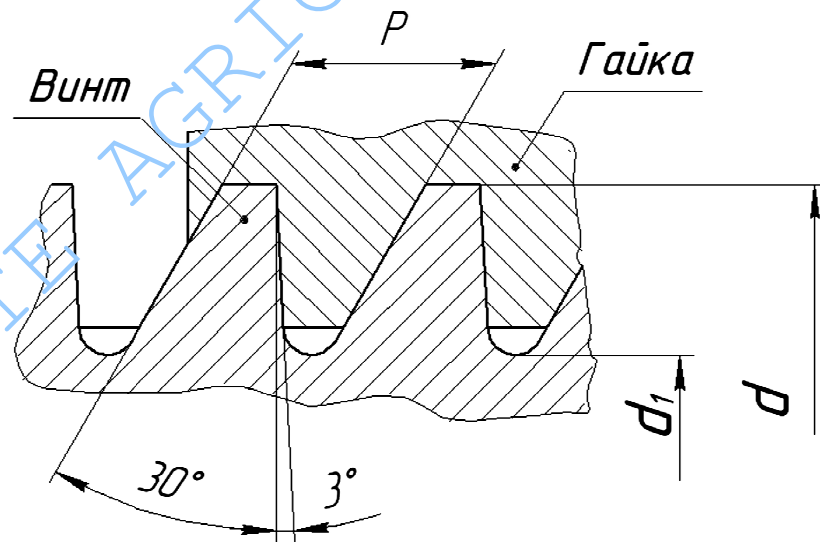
Резьба упорная (ГОСТ 10177-82)
